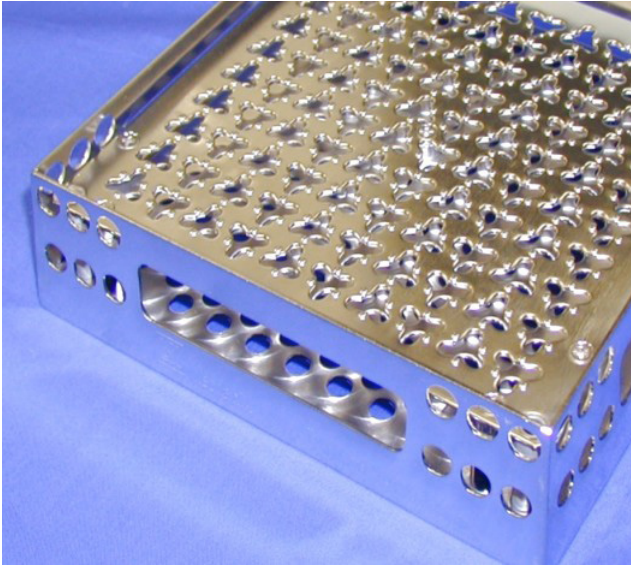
Werkstück-Trägermagazin mit eingearbeiteten Formnestern (LK Mechanik; www.lk-mechanik.de)
